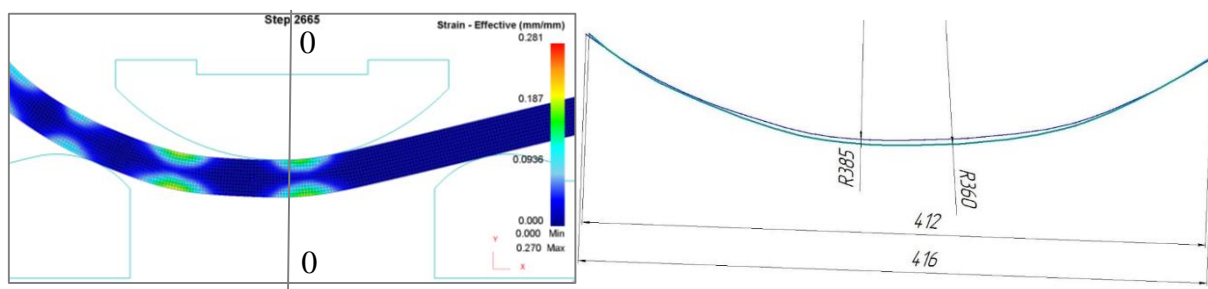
Четвертый шаг: а) деформации трубной заготовки; б) параметры заготовки
